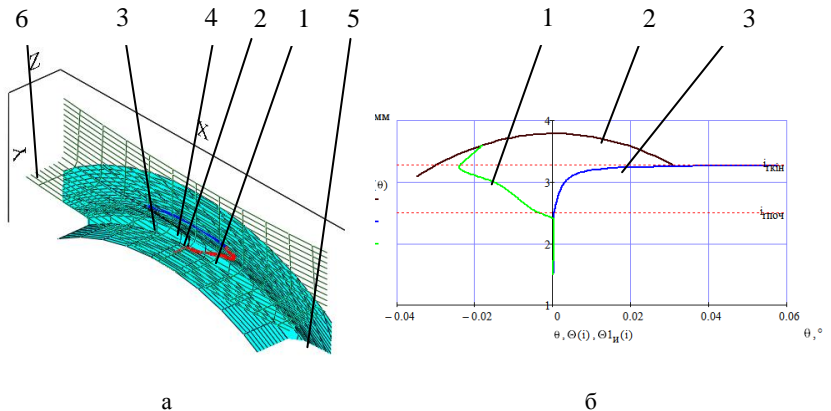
Перетин шліфувального круга і шийки колінчастого вала
